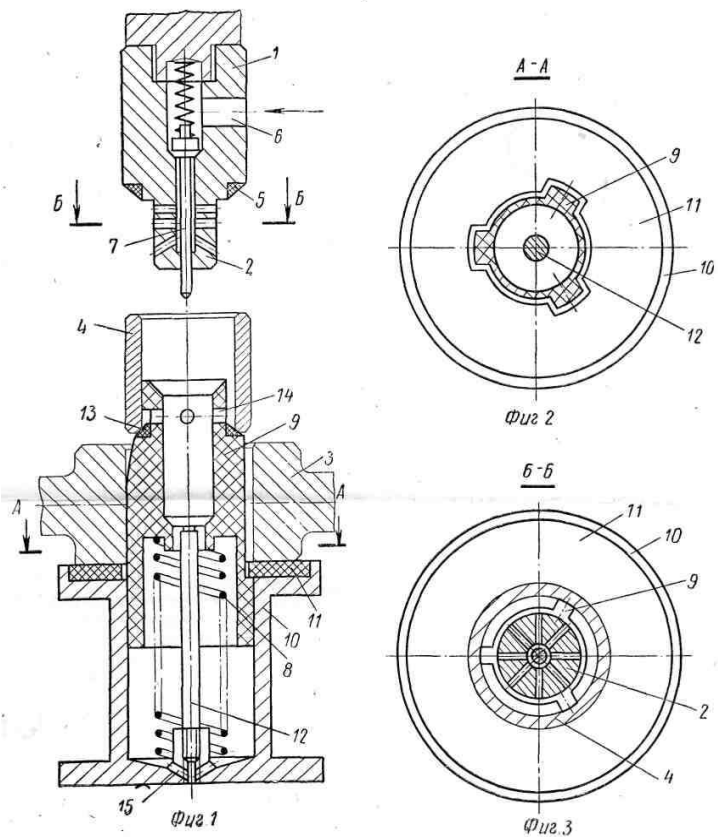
Устройство для термической сборки бронзовых втулок со стальным корпусом
